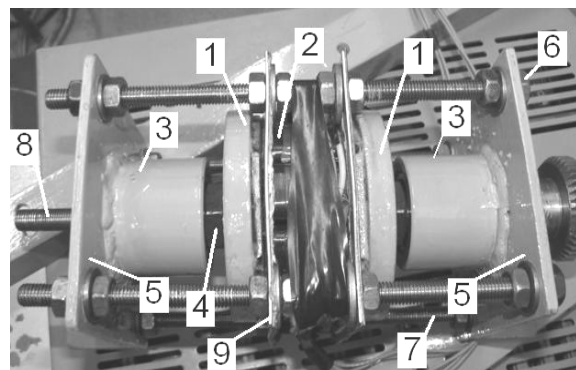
Конструкция макетного образца дискового двигателя: 1) ротор; 2) стержень статора двигателя; 3) подшипниковый узел; 4) контргайка; 5) опора с подшипниковым узлом; 6) гайка прижимного щита; 7) шпилька; 8) вал; 9) прижимной щит
